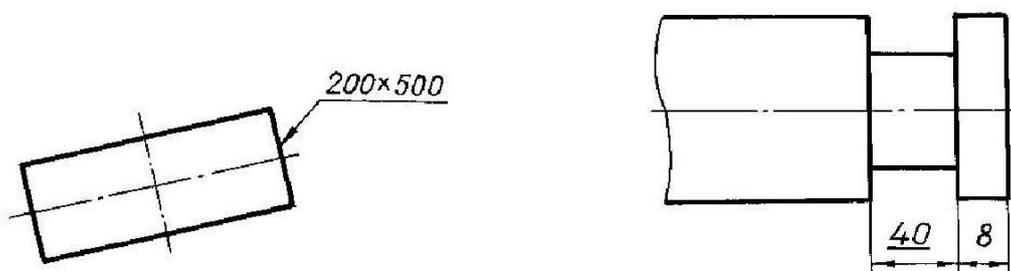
Обозначение размеры детали или отверстия прямоугольного сечения
